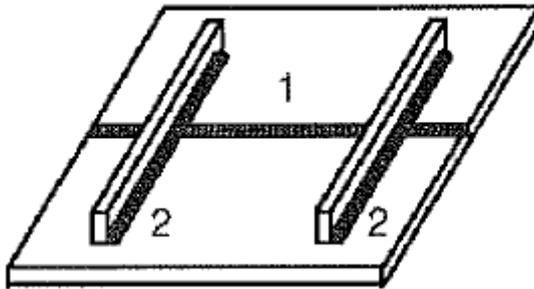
Secuencia de soldeo para reducir las tensiones residuales en uniones soldadas
